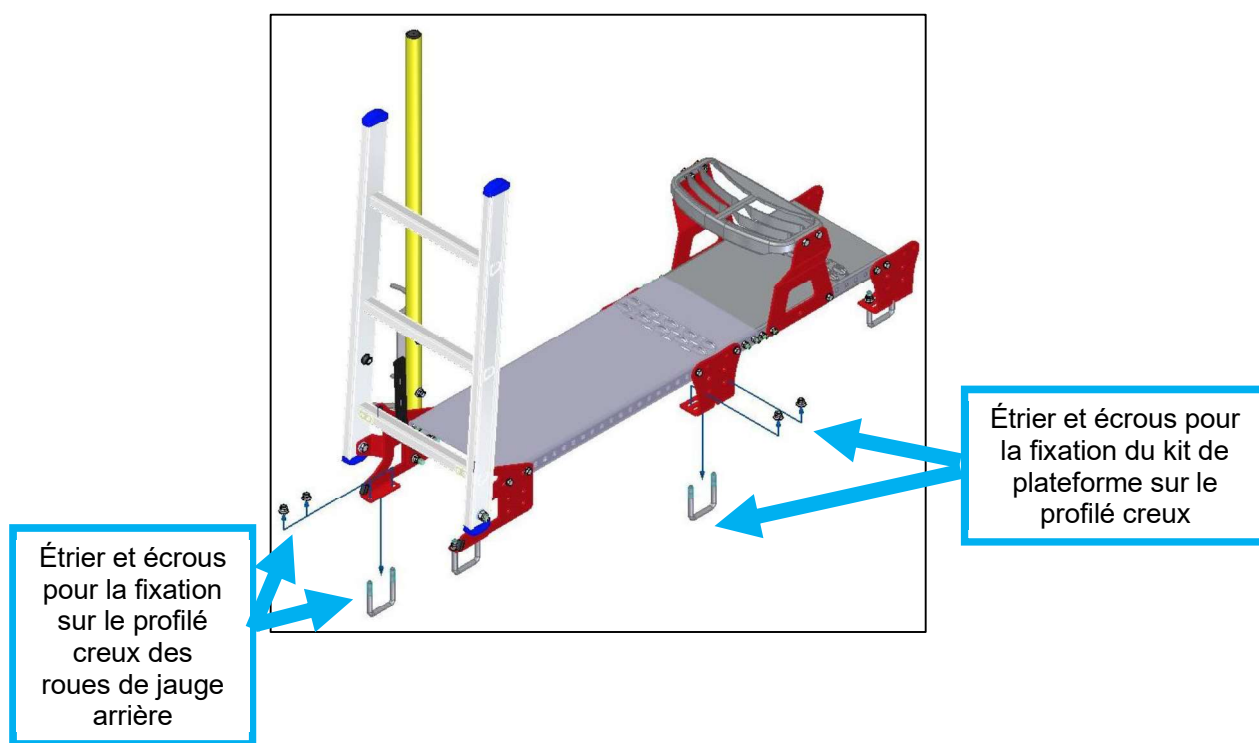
composants du kit de plateforme VS600-1200 avec roue de jauge à l'arrière
